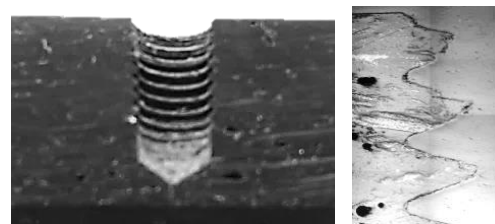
Makroskopische und mikroskopische Aufnahme eines mechanisch eingebrachten Gewindes
